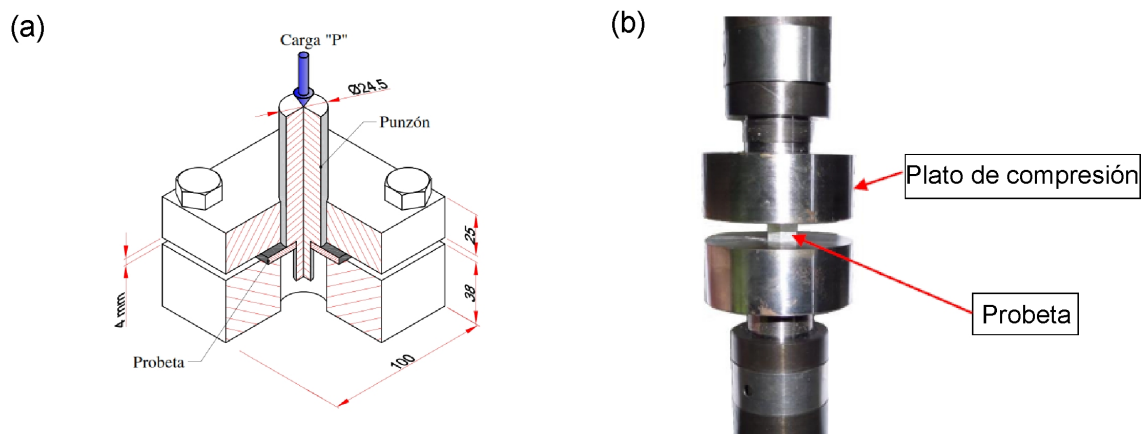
(a) Esquema del ensayo de corte por punzón, (b) Platos de compresión y probeta montada para ensayo de compresión.
